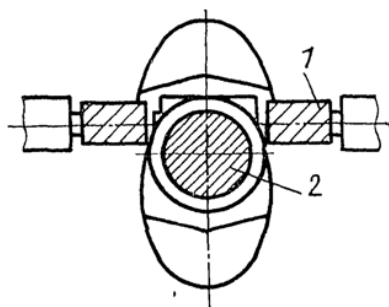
Схема фрезерования установочных площадок на противовесах щеках:
